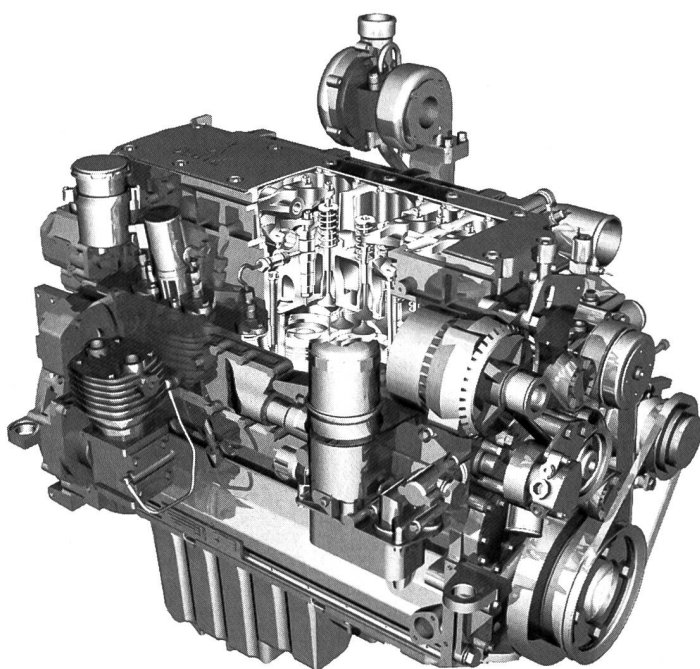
Moderner Dieselmotor DEUTZ, Typ BF6M 2013, 6-Zylinder, Hubraum 5,7 Liter, vier Ventile je Zylinder. Die Einspritzung erfolgt durch Einzelsteckpumpen, Leitung und Einspritzdüsen. Dem Abgasturbolader ist ein Ladeluftkühler nachgeschaltet. Der Motor zeichnet sich aus durch hohe Elastizität, tiefen Verbrauch, günstige Lärm- und Abgaswerte. Eingebaut im Traktor FENDT Favorit 716 Vario, FAT-Test Nr. 1792/99.
